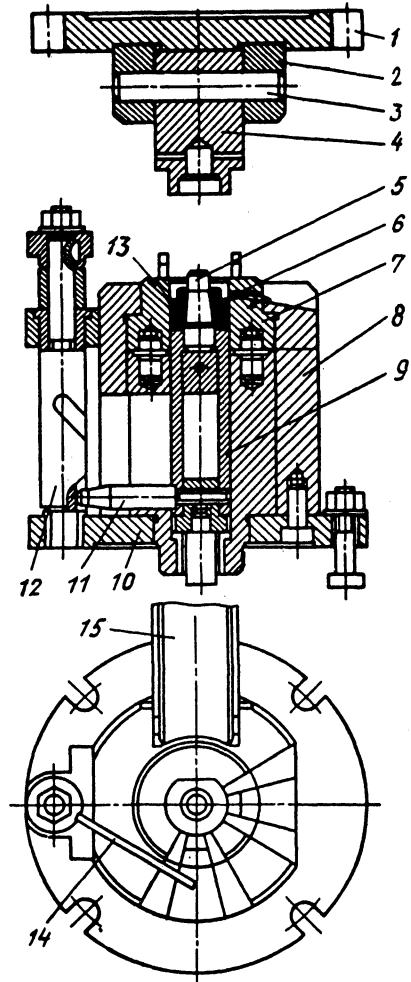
Конструкция пресс-формы для пуансонно-поршневого прессования деталей типа втулок:
